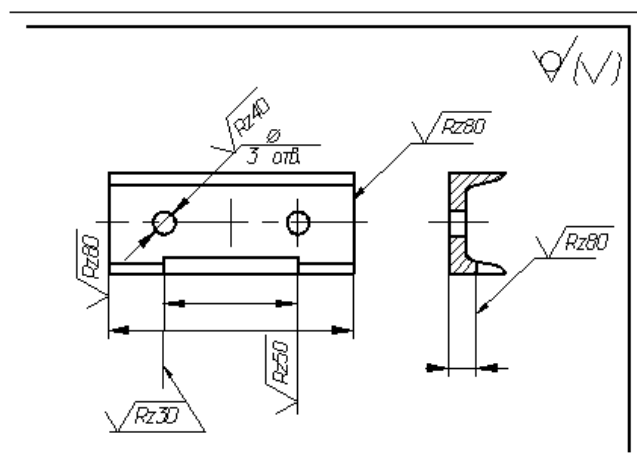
Указание шероховатости когда большая часть поверхностей не обрабатывается по данному чертежу
